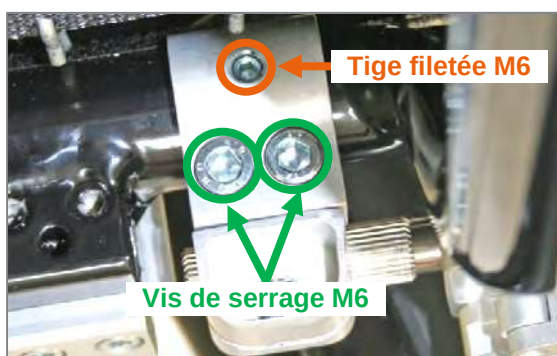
Tige filetée M6 et vis de serrage M6 pour le déplacement du clip de serrage sur le tube de châssis (vue du côté intérieur du produit)
